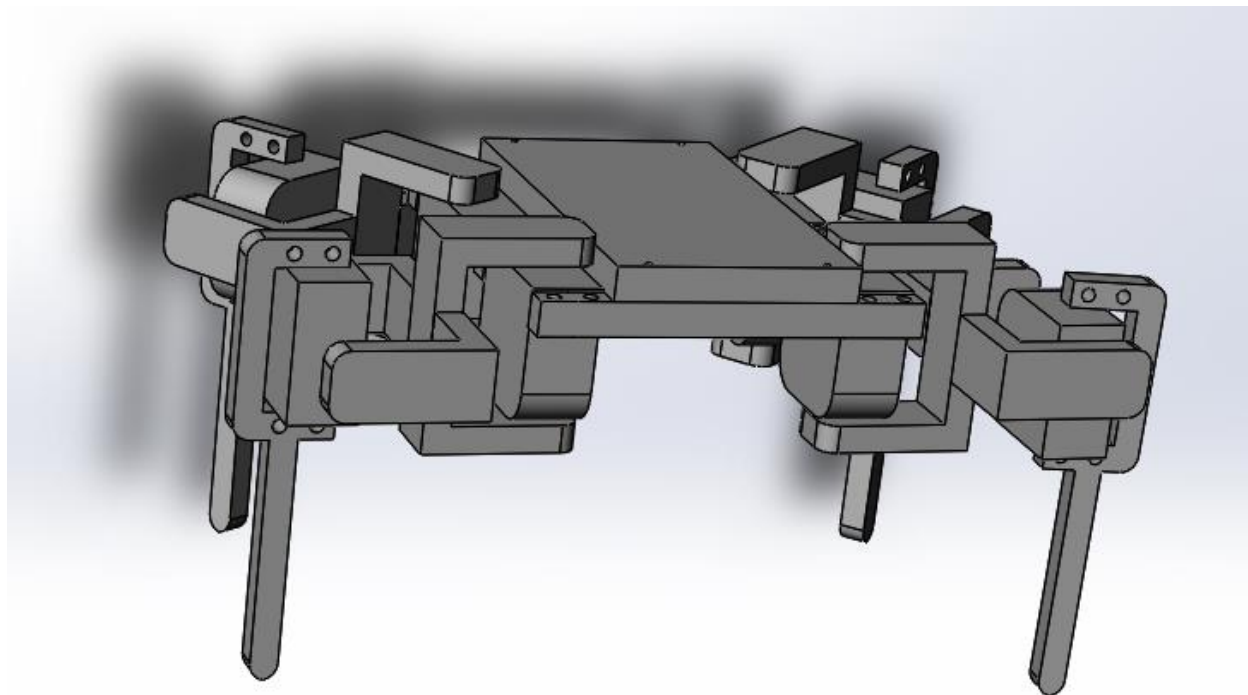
3D-модель готової конструкції крокуючого робота.
